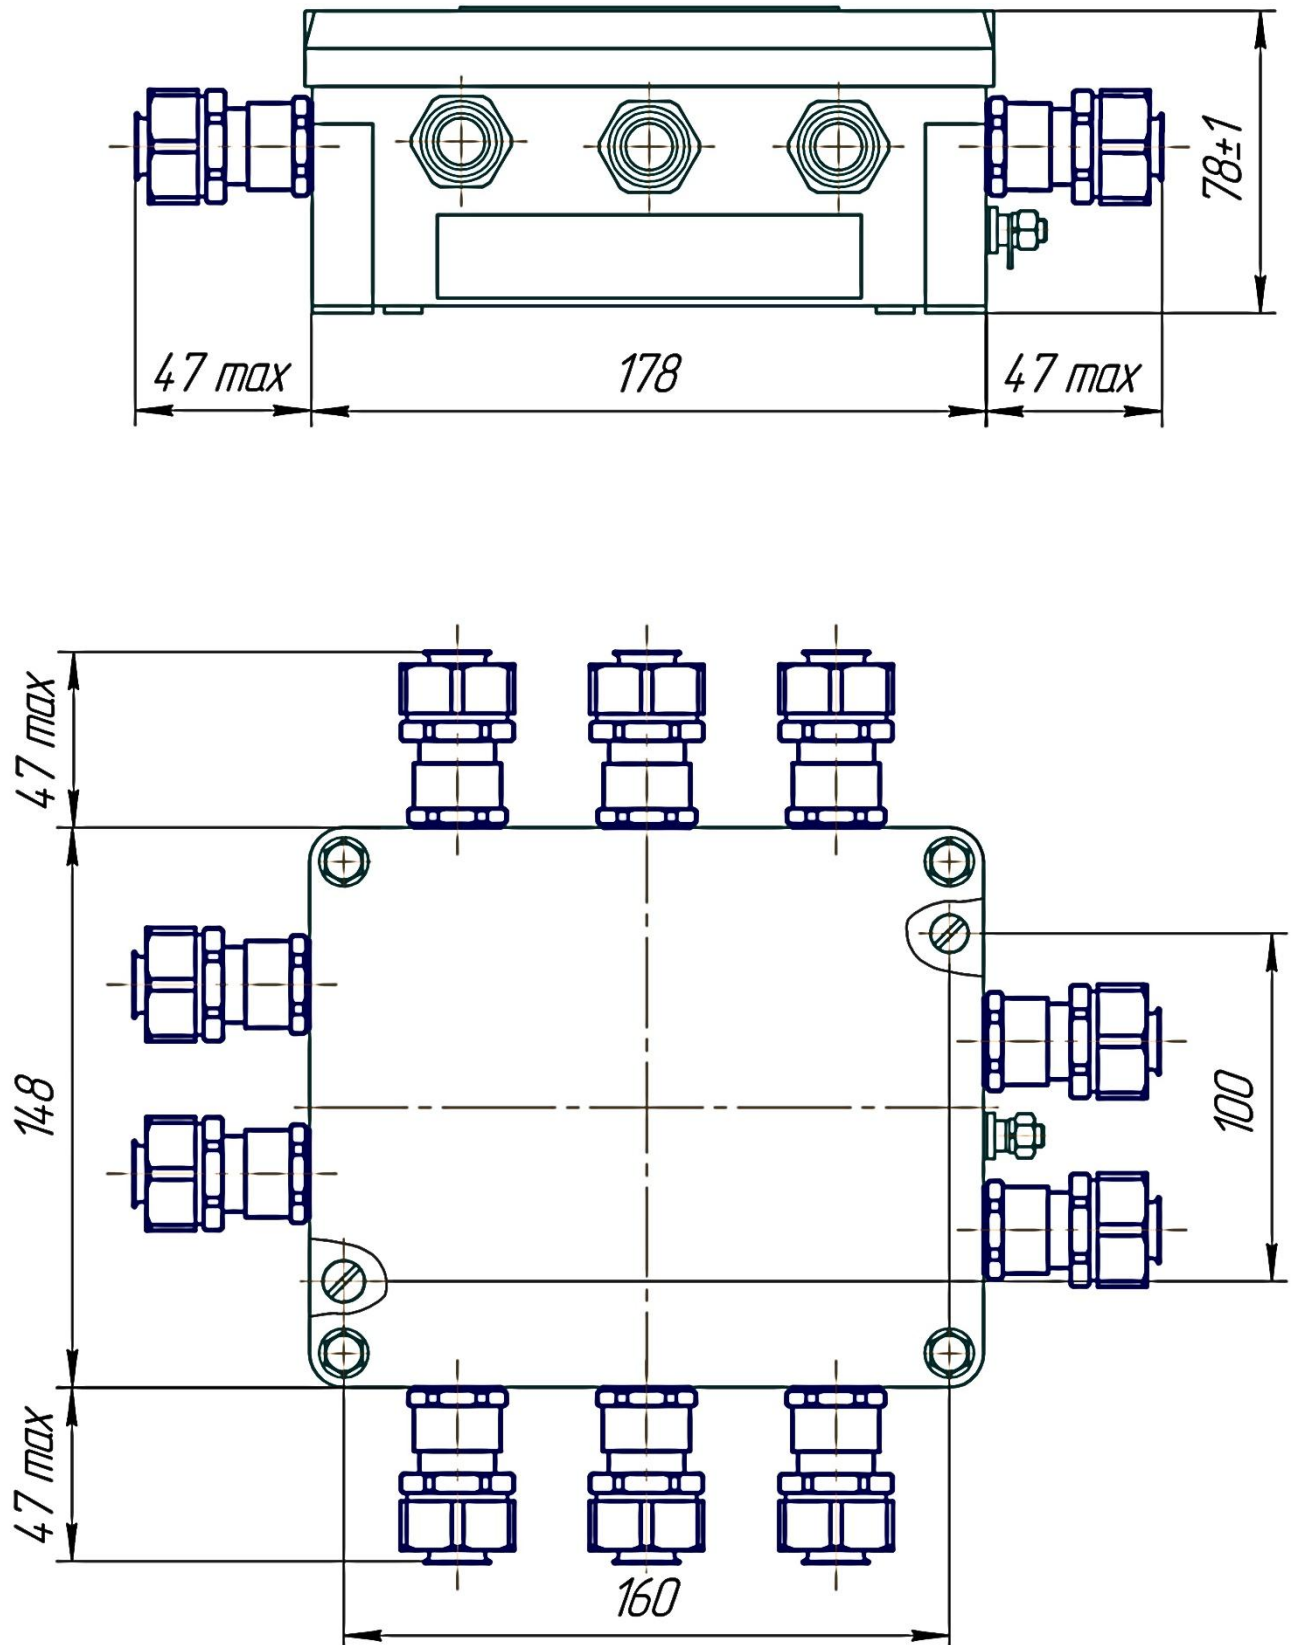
Блок силовой БС. Габаритные и присоединительные размеры
